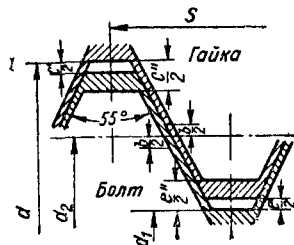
Схема расположения полей допусков дюймовой резьбы.
